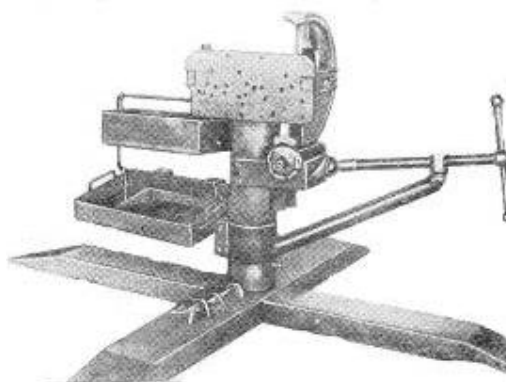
Стенд для сборки и разборки двигателей «ОПР - 989»
